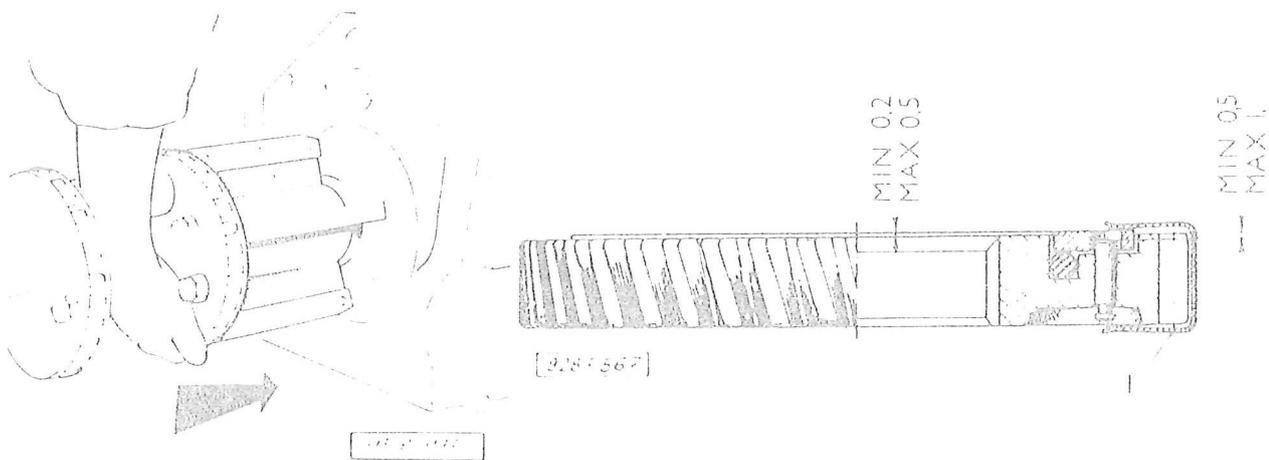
Einschieben der Kurbelwelle mit der Vorrichtung PRM-0023
